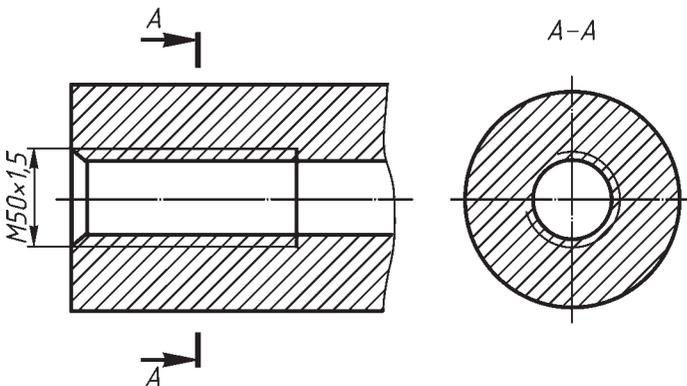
Изображение резьбы в отверстии на разрезе. Обозначение резьбы
